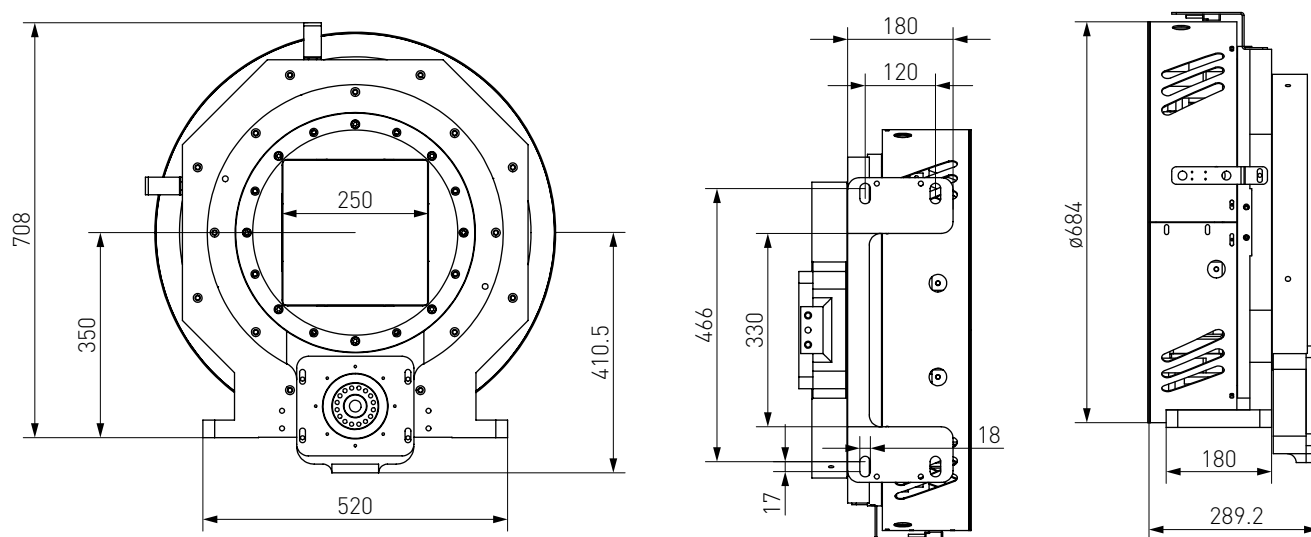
Габаритный чертеж патрона вспомогательного RKQ-240AJYF.
